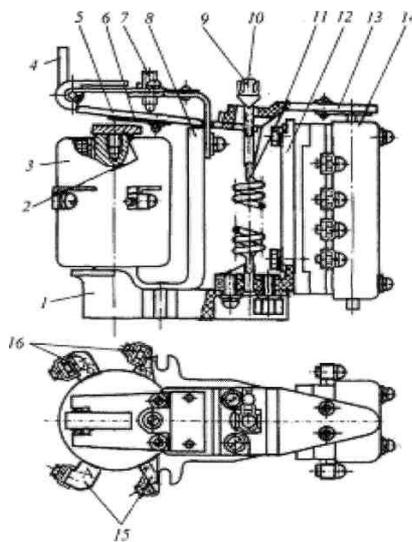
Реле заземления РЗ-303: 1 - изоляционное основание; 2- сердечник; 3 - катушка сигнализатор срабатывания; 5 - якорь; 6 - немагнитная прокладка; 7 -шпилька для регулирования зазора под якорем; 8 - магнитопровод; 9 - гайка; 10- шпилька для регулирования усилий отключающей пружины; 11 - отключающая пружина; 12 -кронштейн для крепления блокировочных контактов; 13 - изоляционная планка; 14 -блокировочное устройство; 15 - выводы включающей обмотки реле; 16 - выводы удерживающей обмотки реле.
